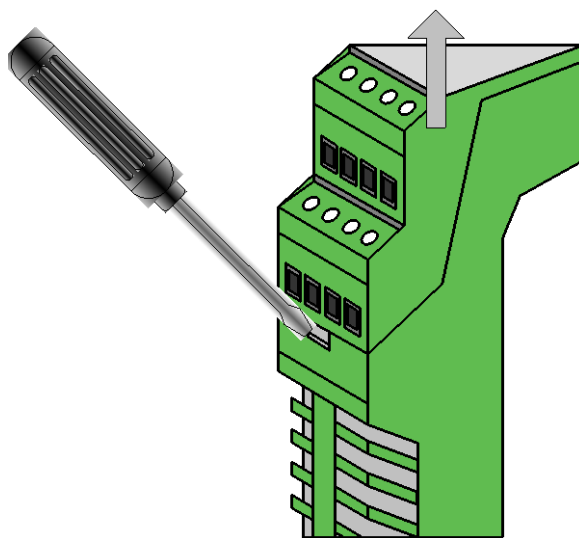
Извлечение платы блока ВИС-4 из корпуса
